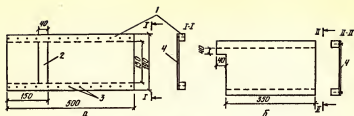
Конструкции шаблонов для разметки паза (а) и шипа (б):
